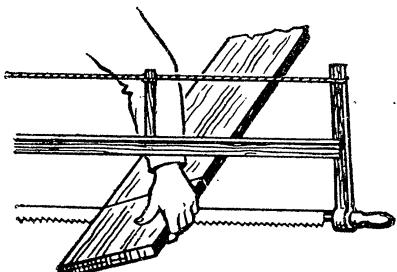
Поддержание рукой отпиливаемой части заготовки для предупреждения брака при пилении
